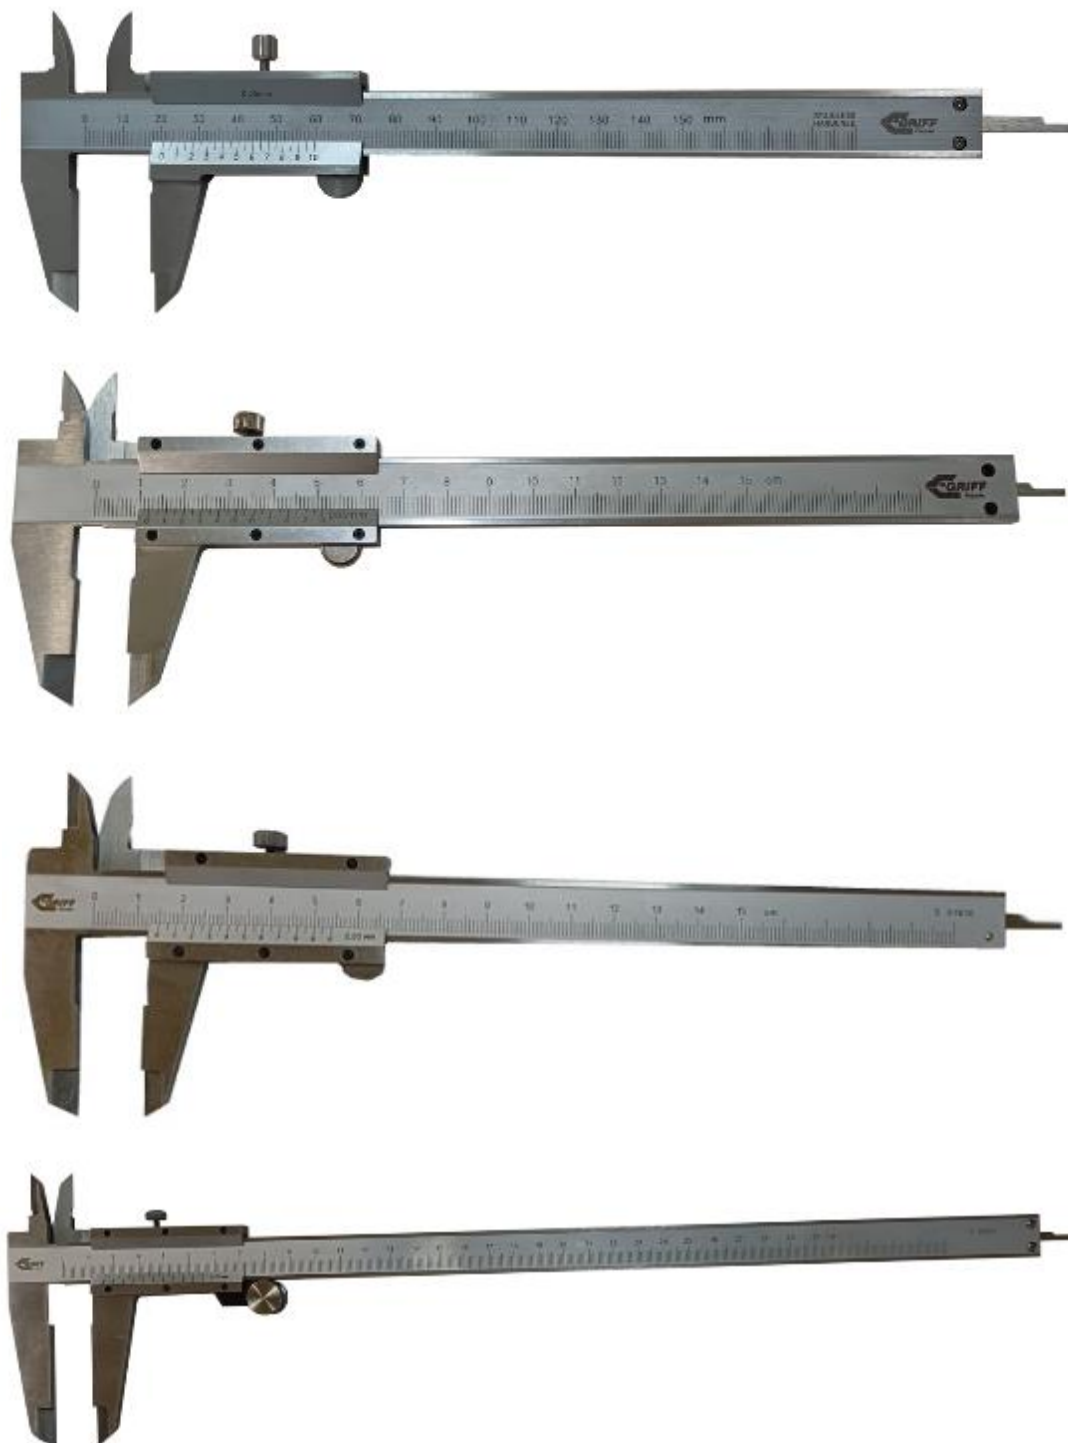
Общий вид штангенциркулей модификации ШЦ-I
